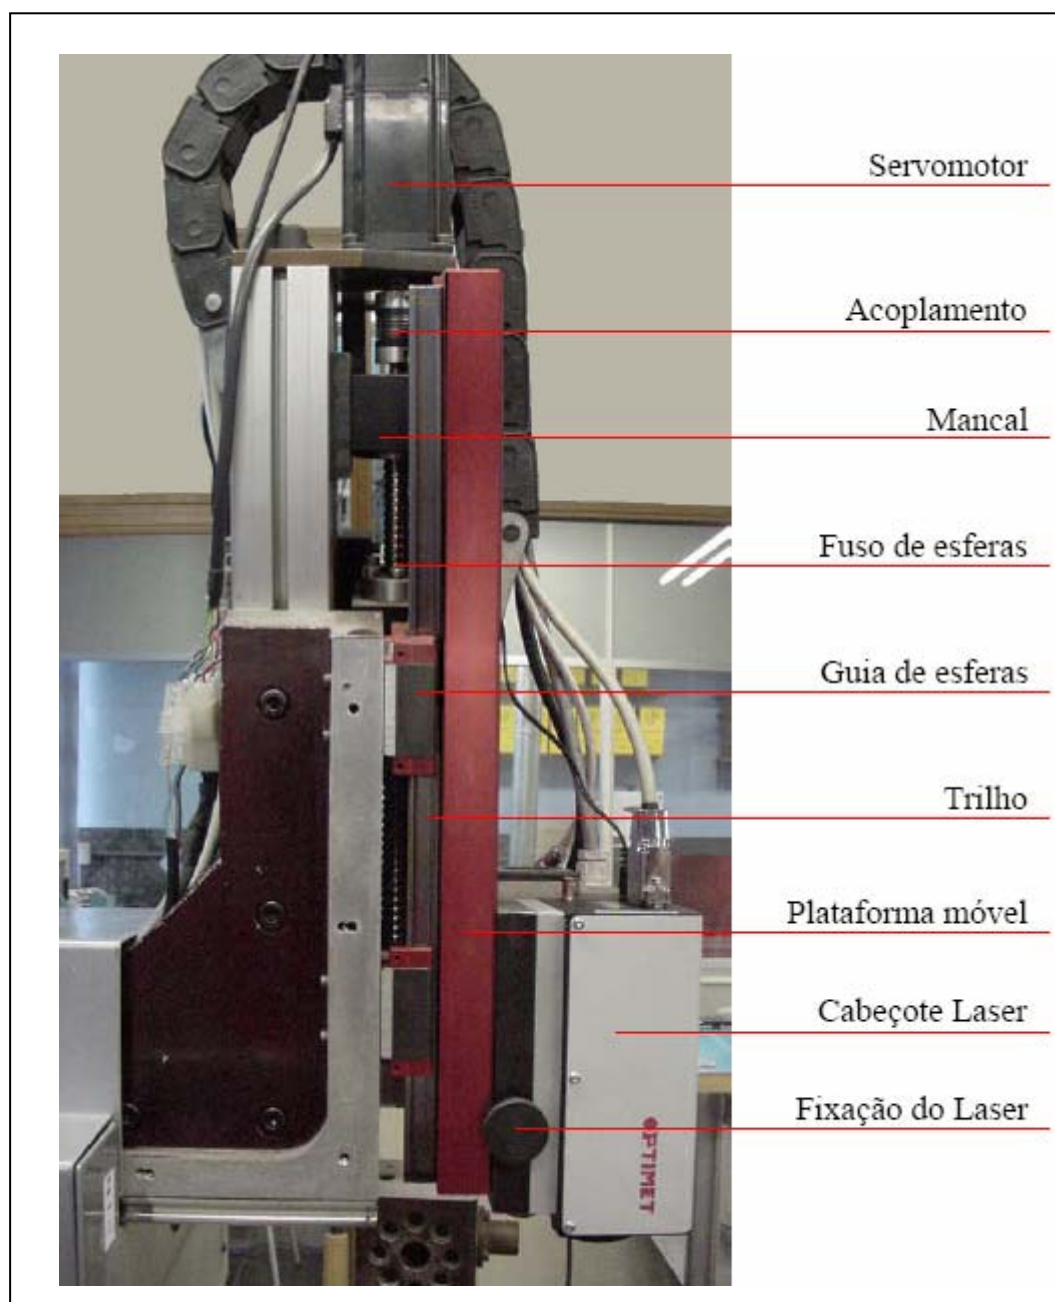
Funcionamento do eixo Z do equipamento CNC Digimill 3D.
